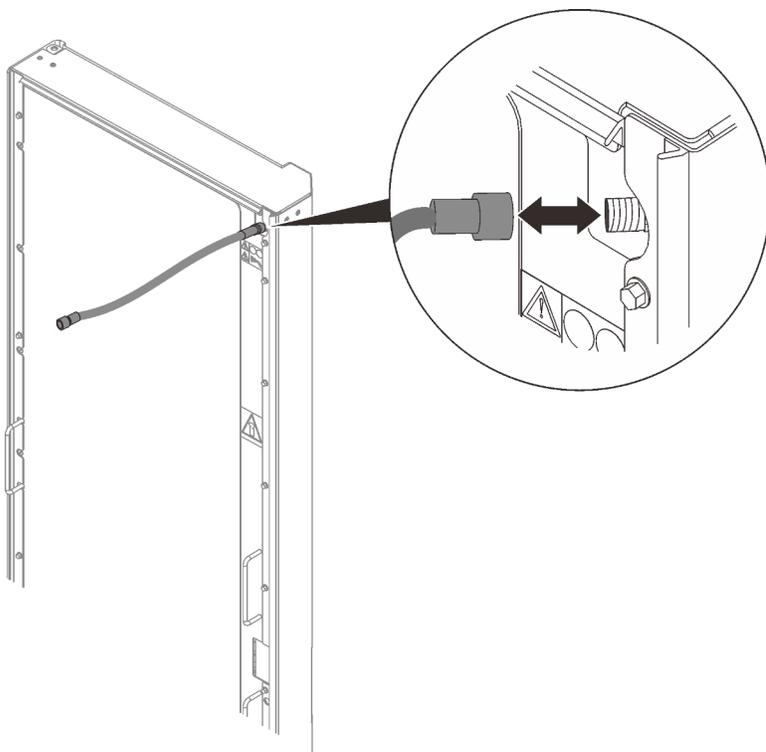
Вставка удлинительного шланга инструмента для удаления воздуха
